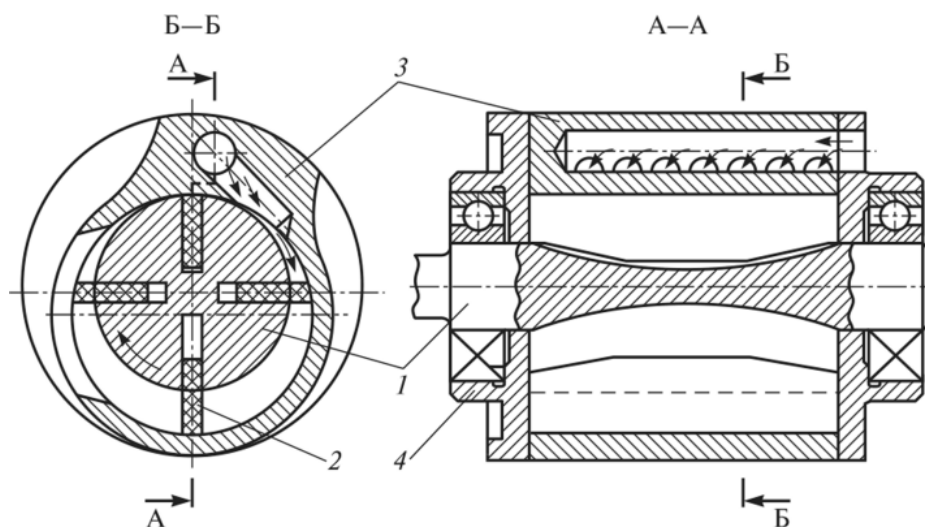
Загальний вигляд ротаційного пневмодвигуна:
